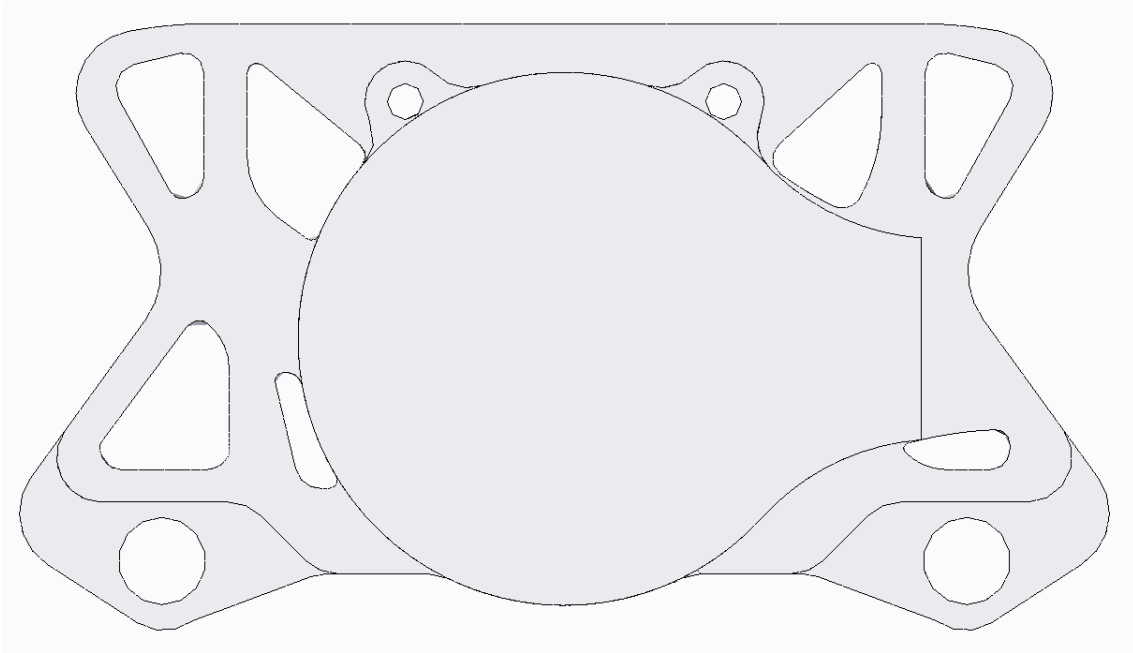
Alzado de la pieza final. Fuente: elaboración propia
